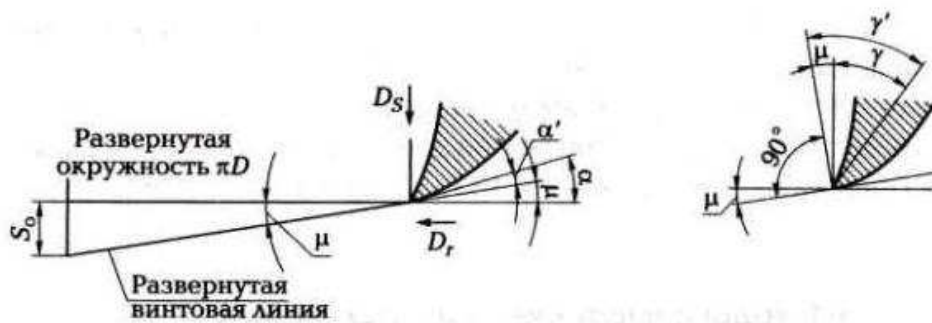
Углы режущих кромок сверла в процессе резания: γ и α – статические передний и задний углы; γ' и α' – действительные передний и задний углы; μ – угол подъема; S_0 – подача на оборот; D_r – направление главного движения (вращения сверла); D_s – направление движения подачи
